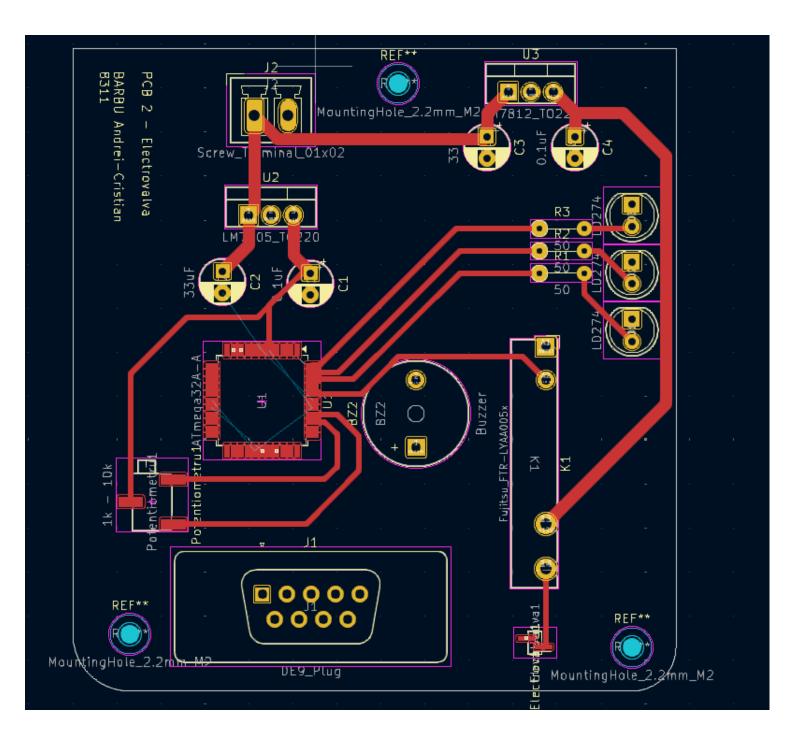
Cablaj imprimat din KiCad (Front Layer)
